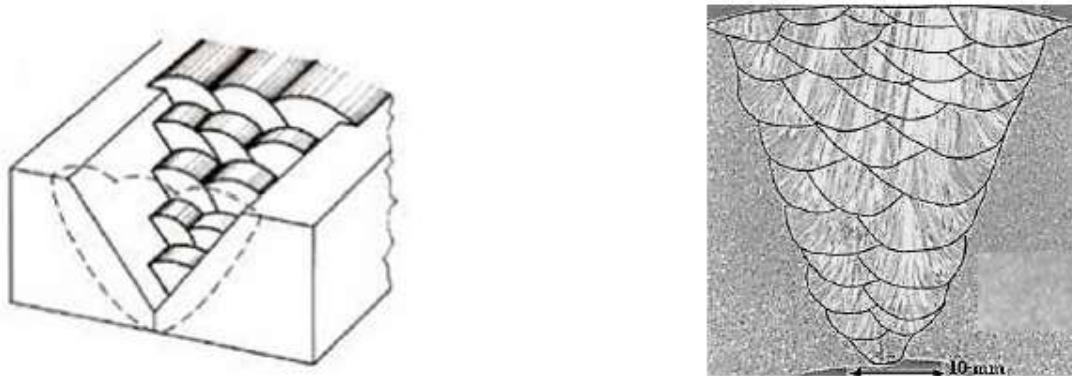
Schéma de la structure d'un joint soudé par du soudage multi-passes et soudure multi-passes à l'électrode enrobée en configuration rectiligne sur un acier inoxydable [8].
